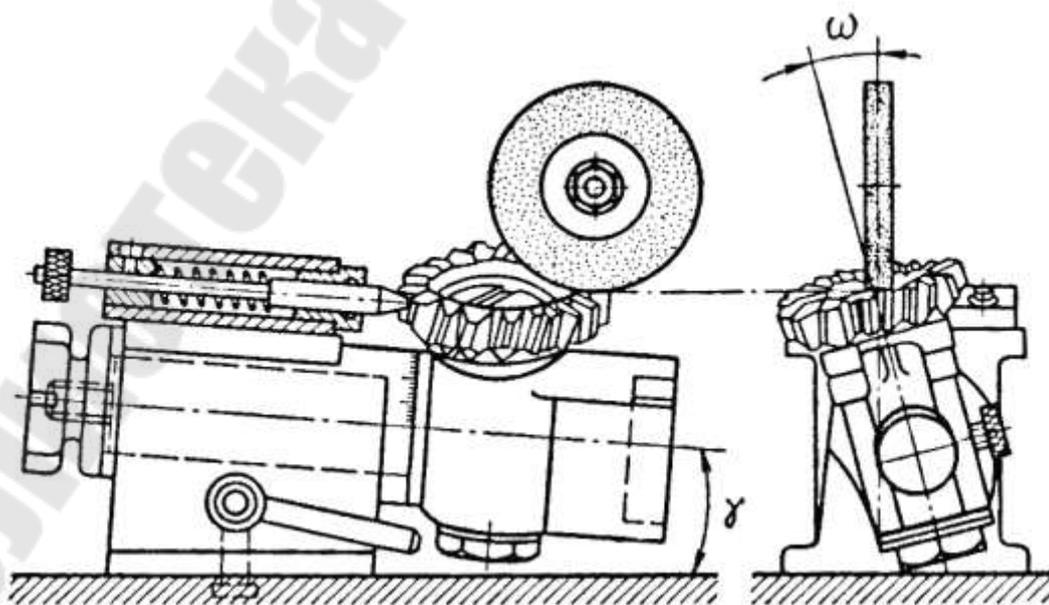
Приспособление для заточки косозубых долбяков на универсально-заточном станке.
